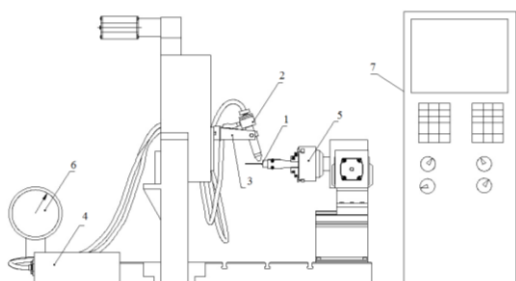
Схема экспериментальной установки для нанесения диффузионного дискретного покрытия: 1 – образец; 2 – сопло; 3 – крепежная стойка; 4 – блок питания; 5 – шпиндель для закрепления образца; 6 – манометр; 7 – система управления оснащена ЧПУ
